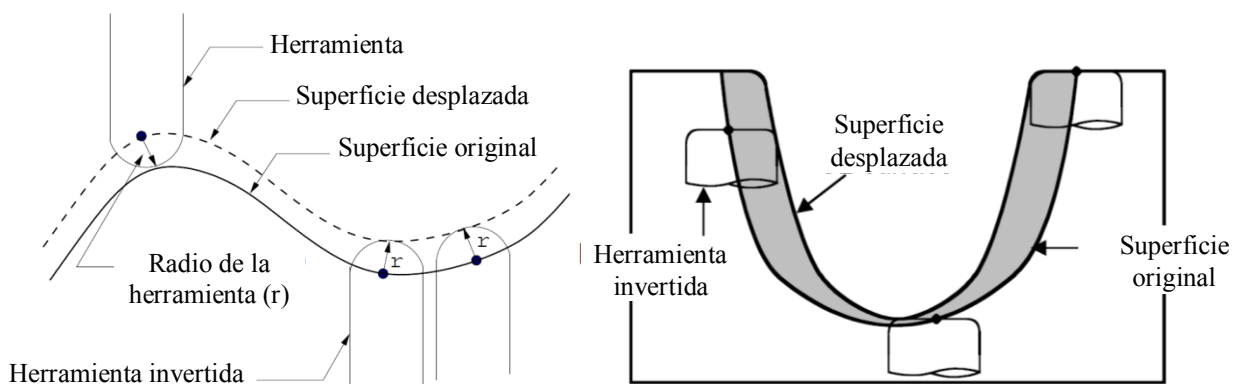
Posicionamiento por inversión de la herramienta: a) herramienta de punta de bola, y b) herramienta de filete.
